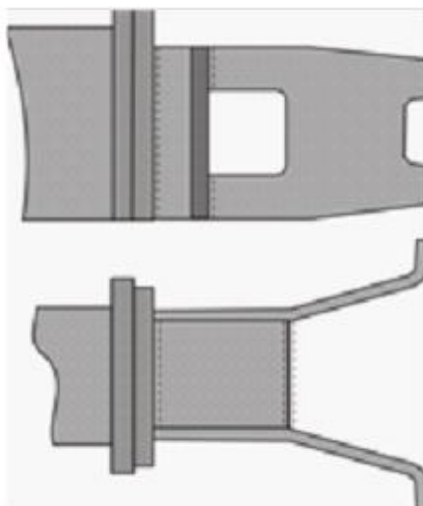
Схема сканирования околошовных зон сварных соединений частей корпуса тормозного блока
